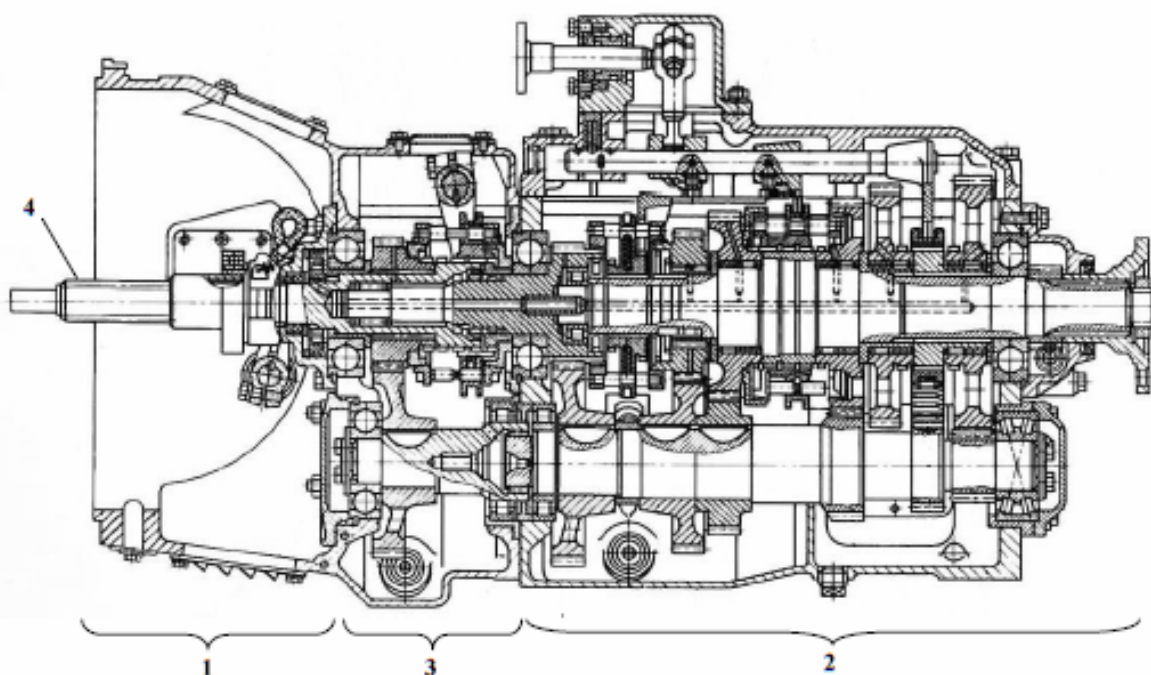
Продольный разрез десятиступенчатой коробки передач КАМАЗ модели 154: 1 – картер сцепления; 2 – основная трехвальная пятиступенчатая коробка передач; 3 – делитель; 4 – первичный вал делителя
